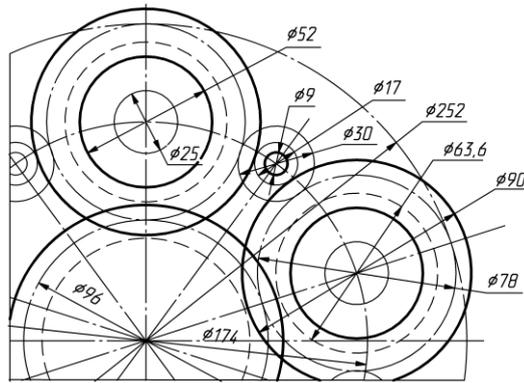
Схема размещения сателлитов и отверстий крепления (фрагмент)
